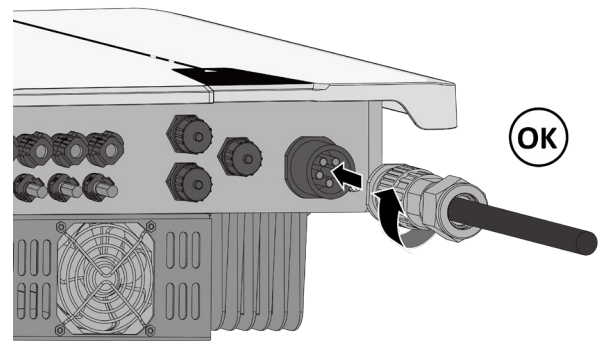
AC-Anschlussstecker mit dem Gerätestecker einrasten
